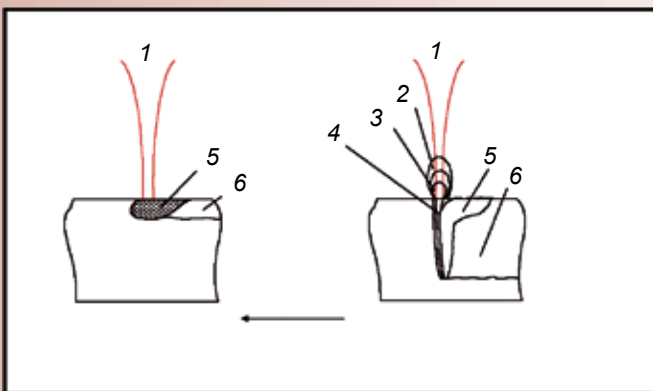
Принципы процесса лазерной сварки: 1 – лазерный луч; 2 – пары металла; 3 – индуцированная лазером плазма; 4 – паровой плазменный канал; 5 – зона сварки (жидкая); 6 – зона сварки (твердая).
